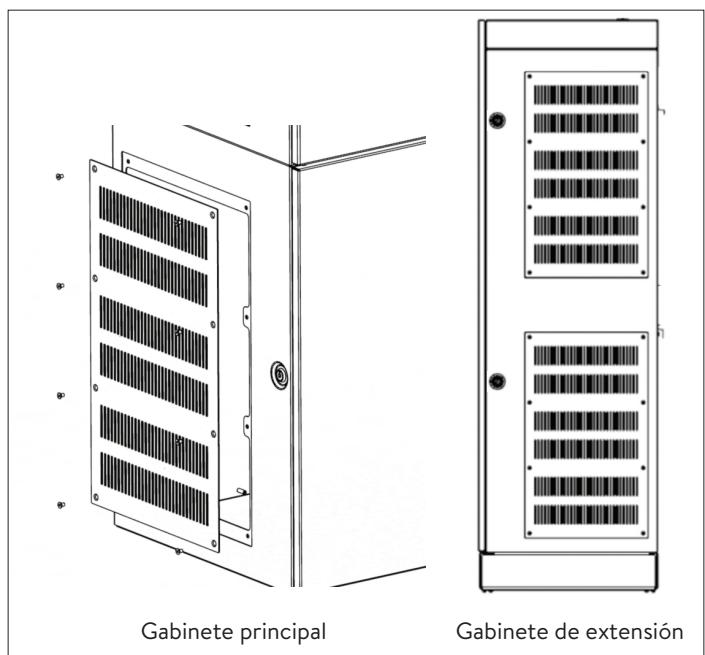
Extracción de la cubierta del panel de acceso del gabinete de baterías
